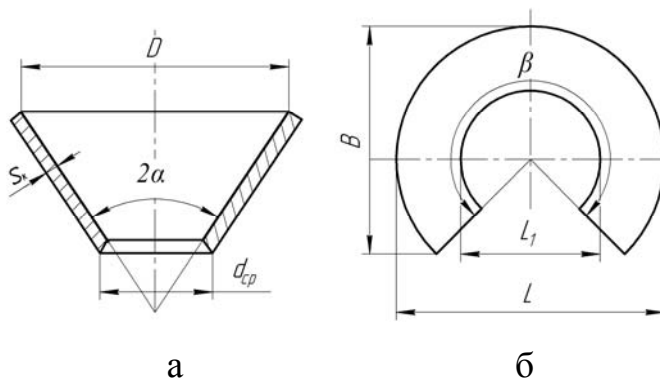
Схема конічного невідбортованого днища: а – головний вигляд; б – розгортка
